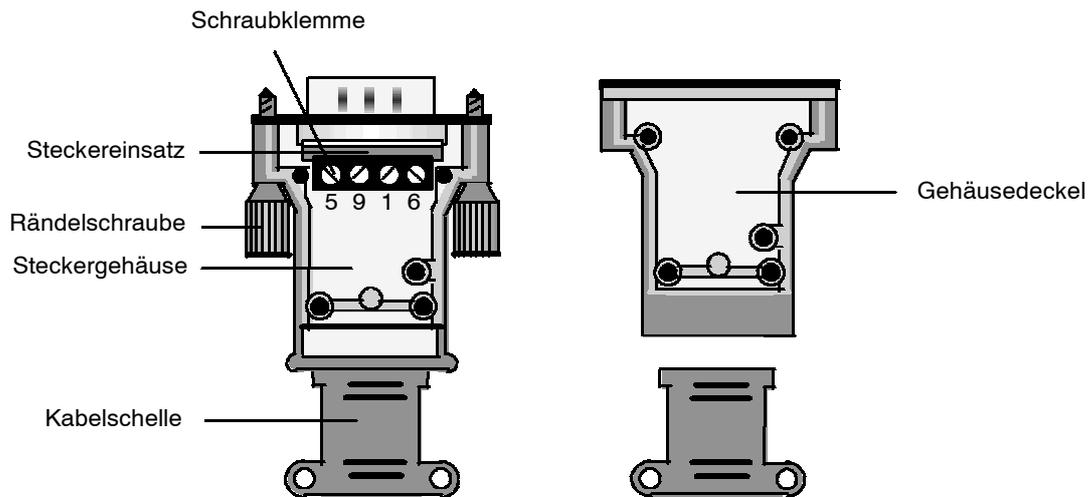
Industrial Twisted Pair Sub-D-Stecker (9-polig) für Selbstmontage
